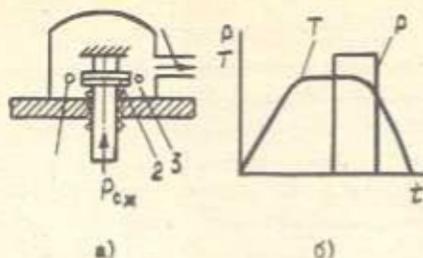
Диффузионная сварка: а) схема сварки; 1 - нагреватель; 2 - заготовки; 3 - камера; б) циклограмма сварки; P - усилие сжатия; T - температура; t - время
